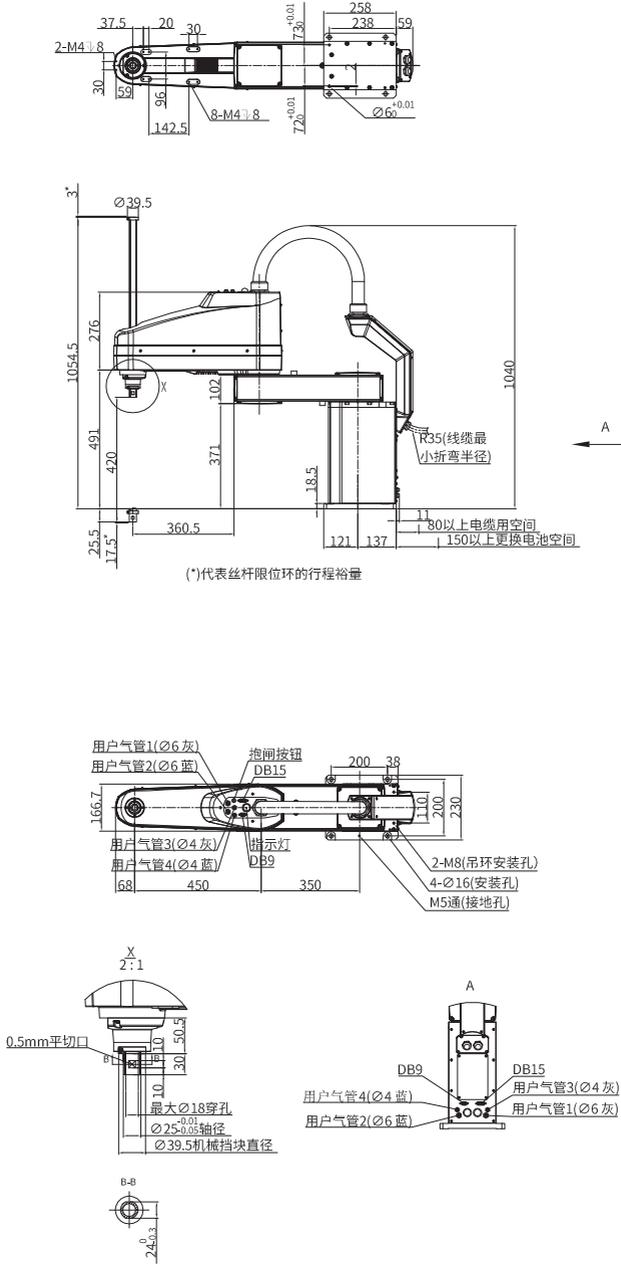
IRB111-20-80Z42TS3 安装尺寸
